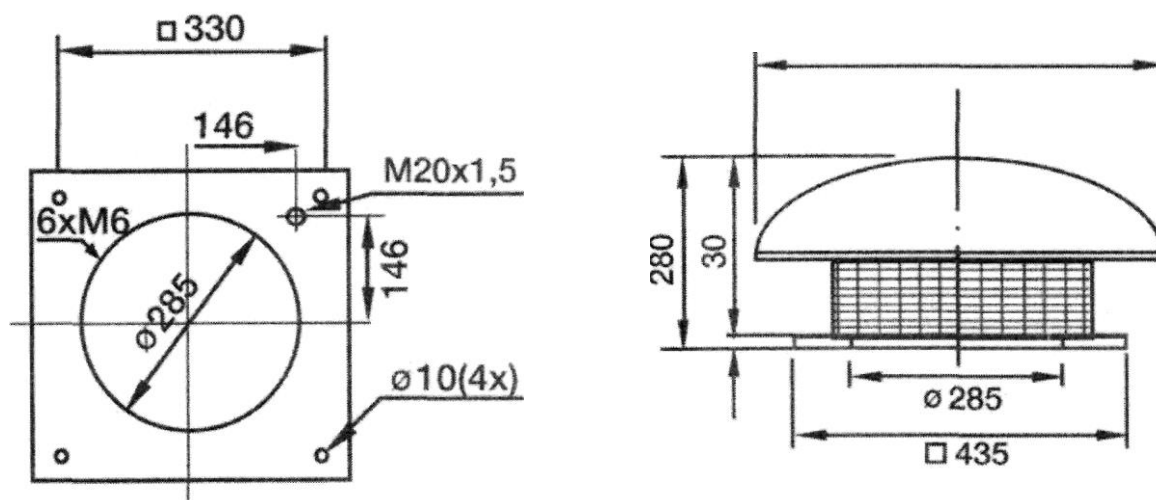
Габаритні розміри вентилятора DHS 311EV
